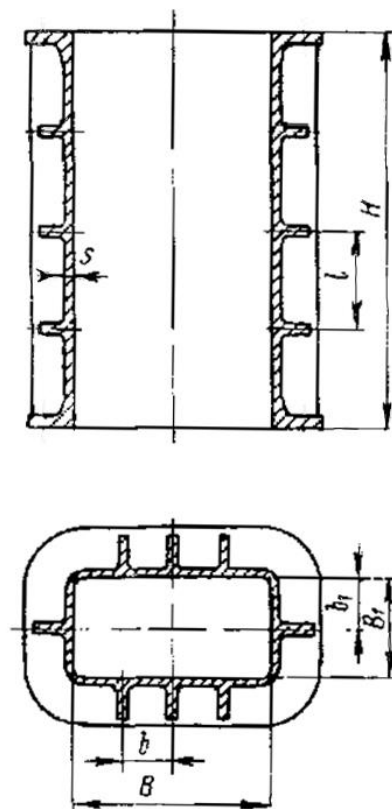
Схема укрепления коробчатой обечайки с продольным и поперечным расположением ребер.
